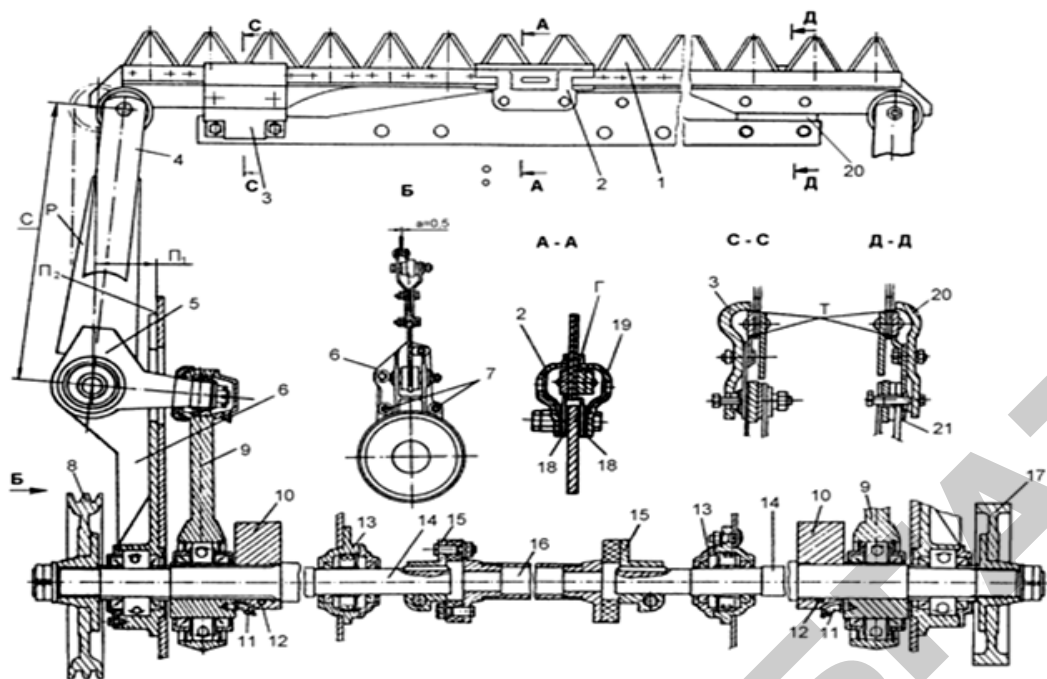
Регулировка беспальцевого режущего аппарата жатки для трав;
